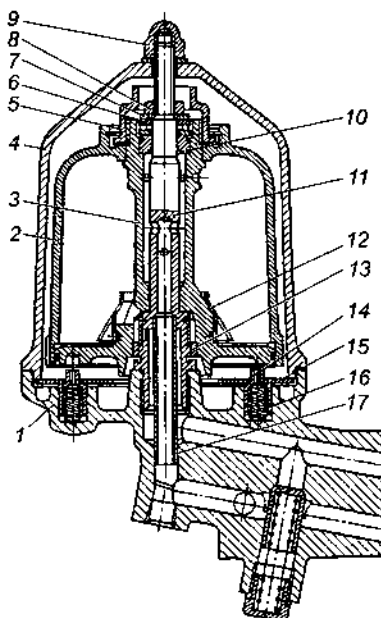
Центробежный масляный фильтр: 1 — корпус; 2, 4 — колпаки ротора и фильтра соответственно; 3 — ротор; 5 — гайка крепления колпака ротора; 6 — упорный шарикоподшипник; 7 — упорная шайба; 8, 9 — гайки крепления ротора и колпака фильтра, соответственно; 10, 13 — верхняя и нижняя втулки ротора; 11 — ось ротора; 12 — экран; 14 — палец стопора; 15 — пластина стопора; 16 — пружина стопора; 17 — трубка отвода масла
